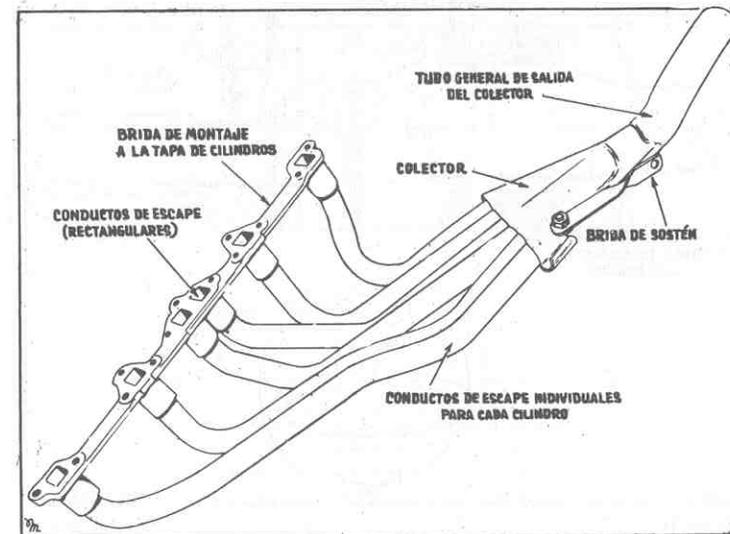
Múltiple de escape del motor 221 SP. Vista desde la brida de montaje.
